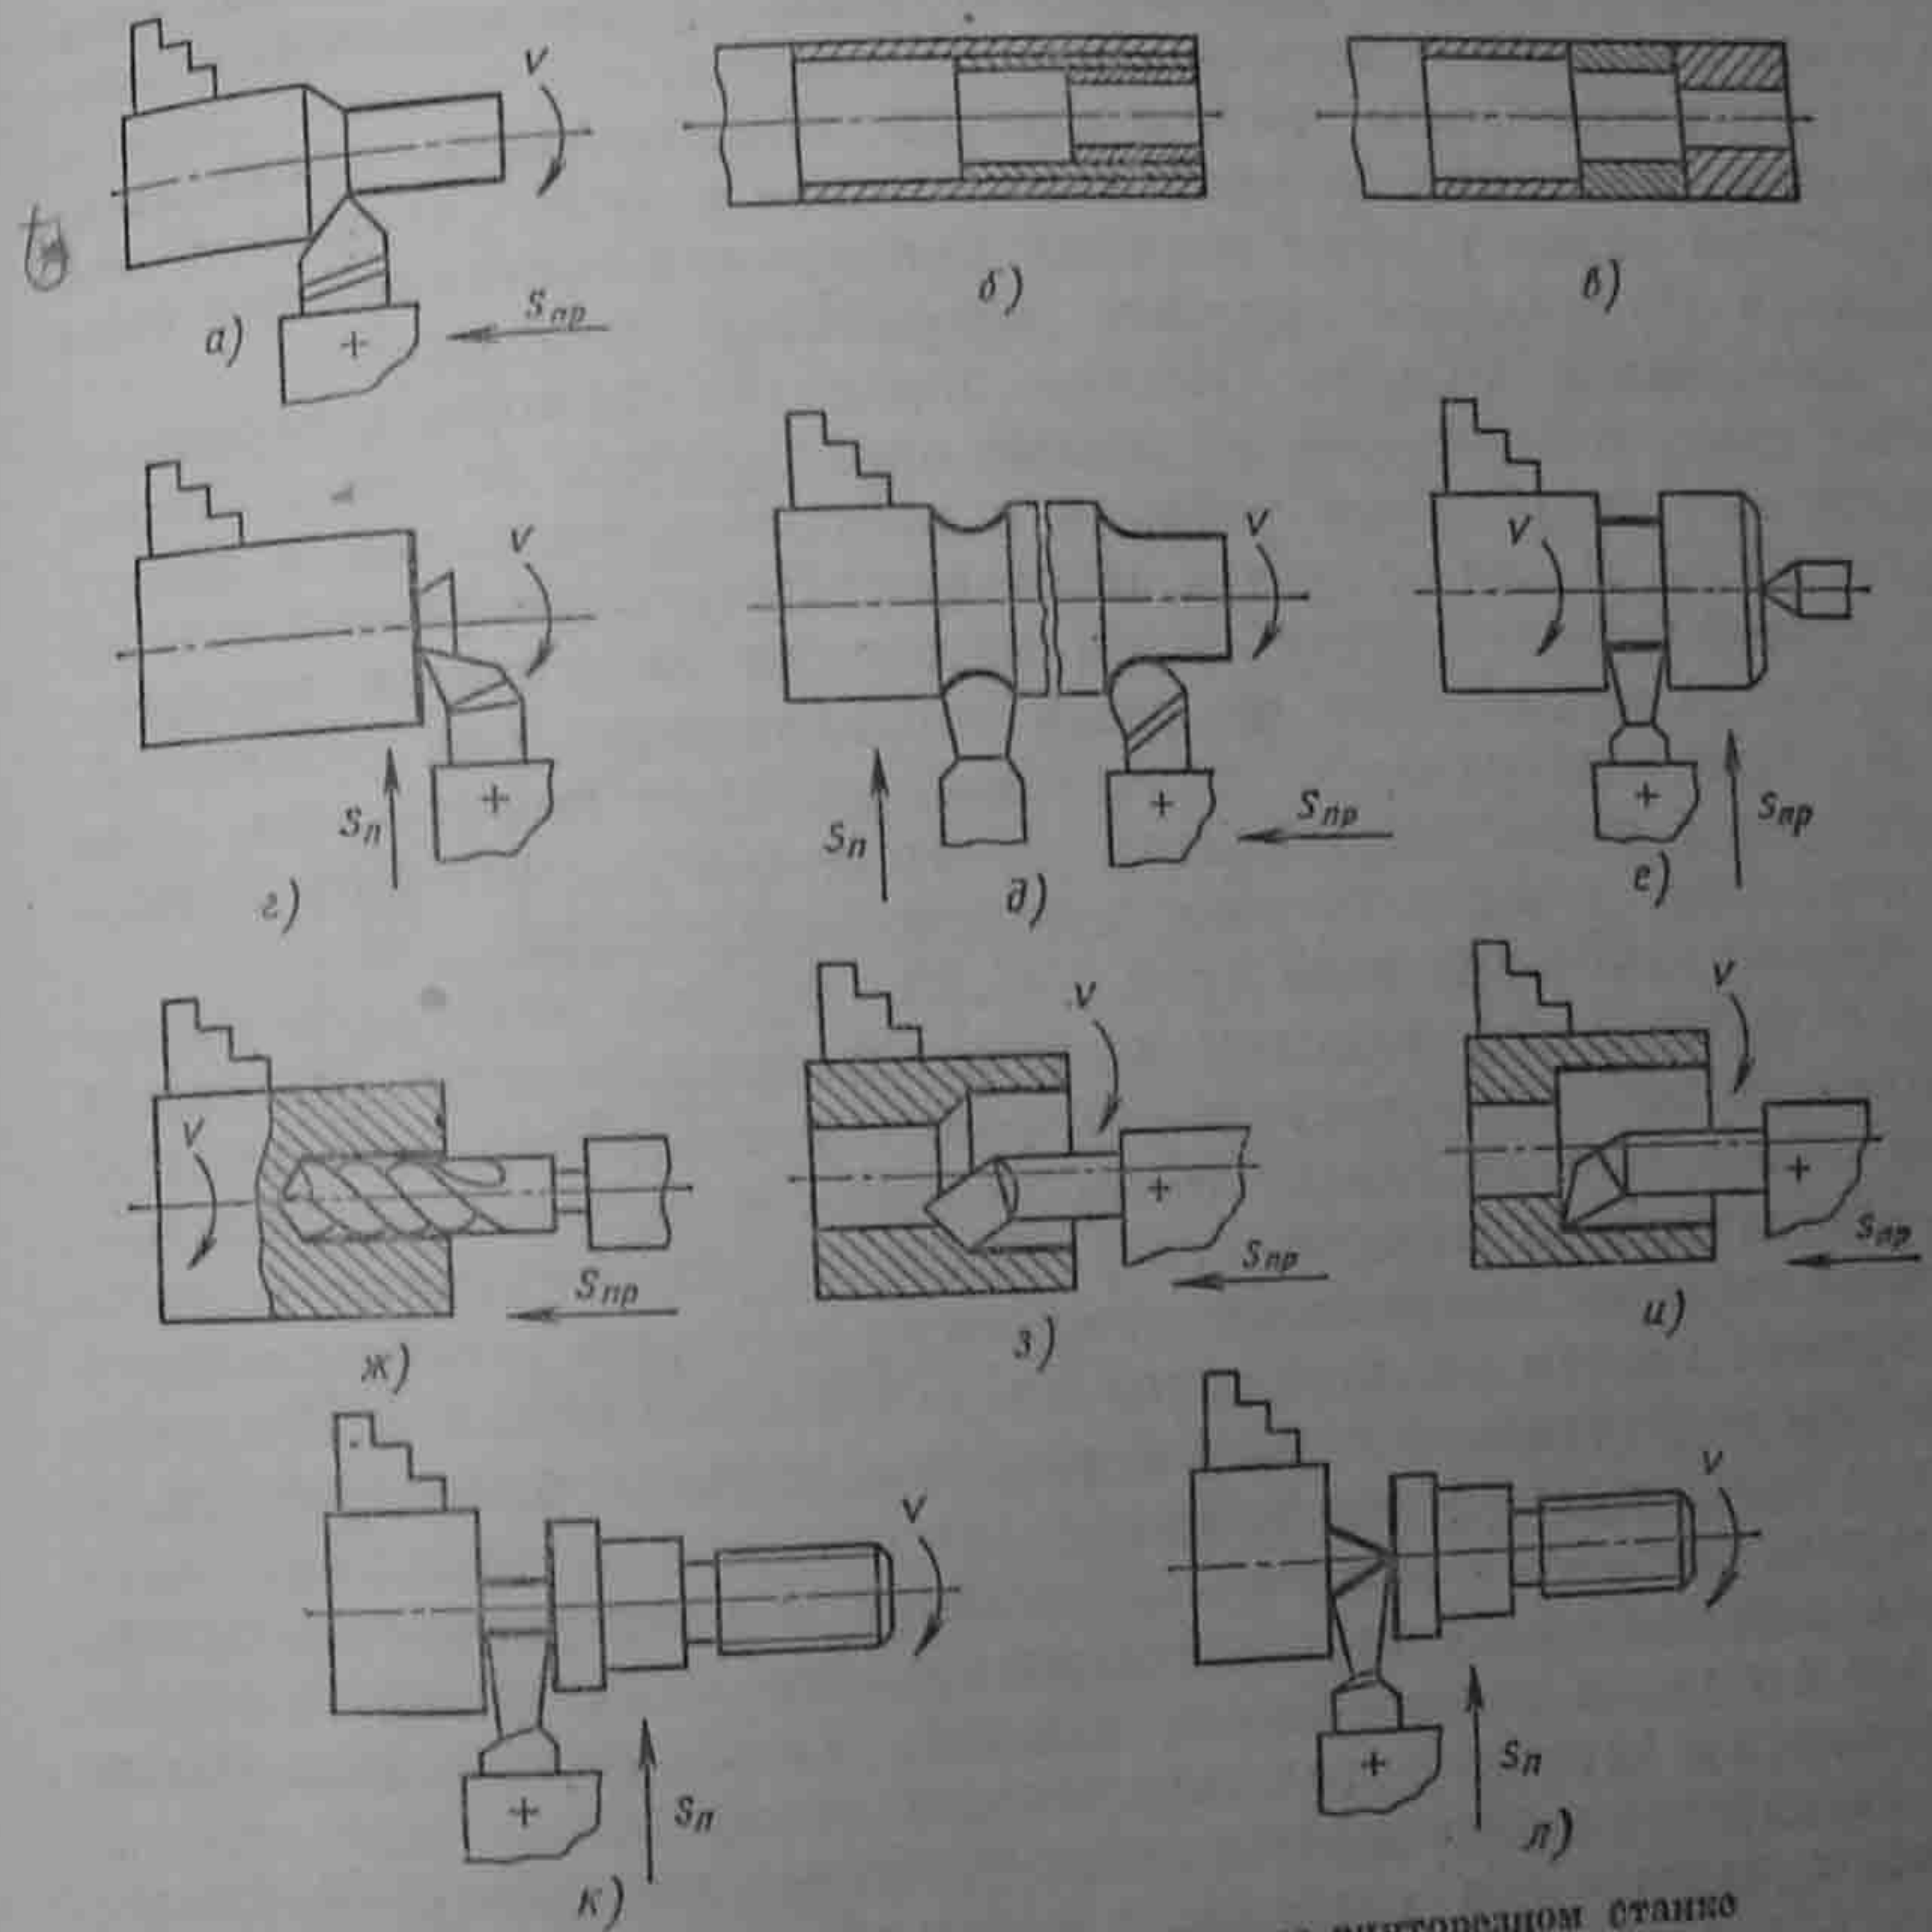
Схемы обработки заготовок на токарно-винторезном станке
